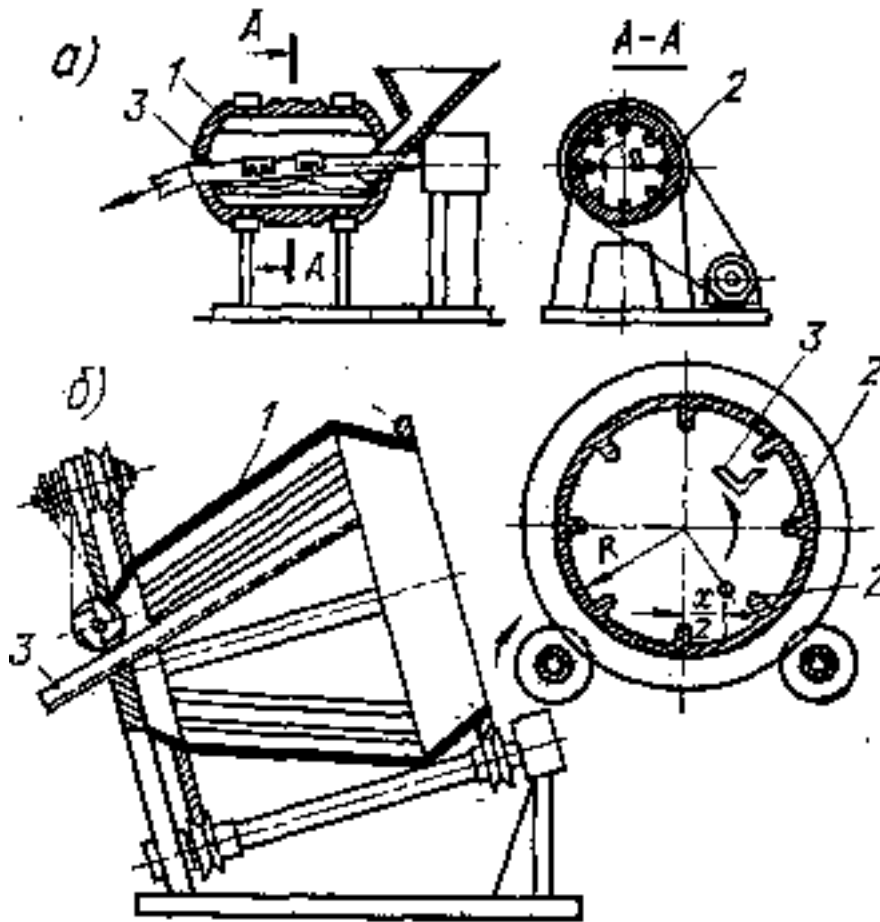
Бункерные загрузочные приспособления с барабаном:
